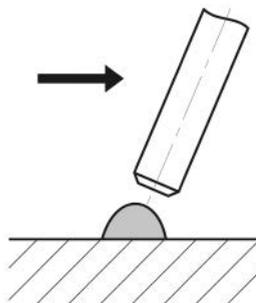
Влияние длины дуги и скорости сварки.
